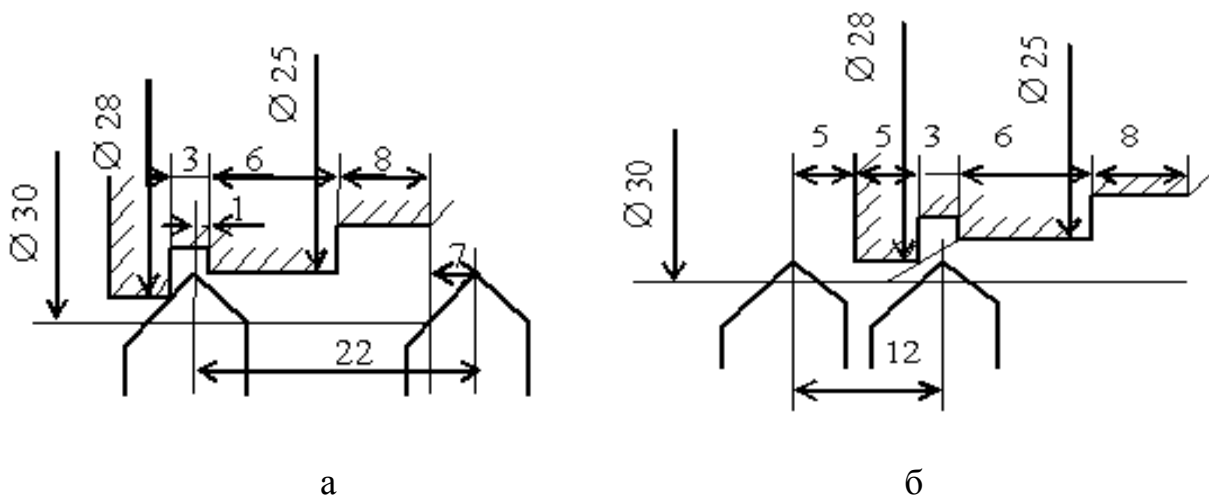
Схема положення інструменту і кінця проходу для обробки:
